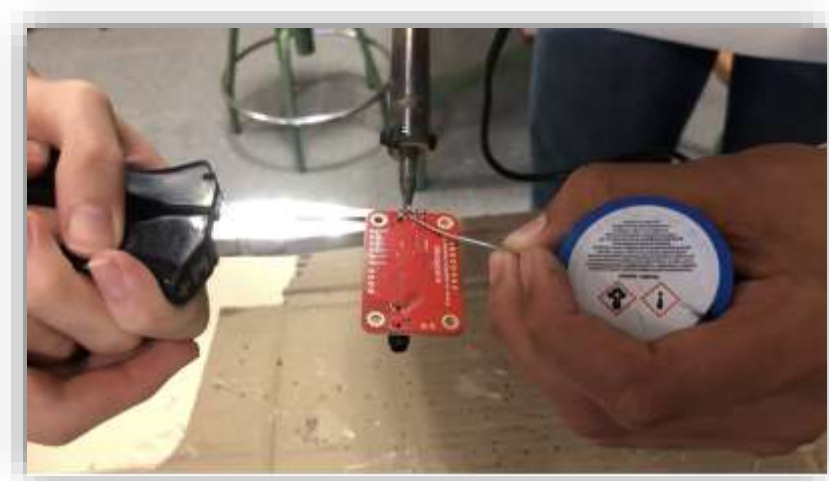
Soldadura del módulo de reconocimiento de voz.
